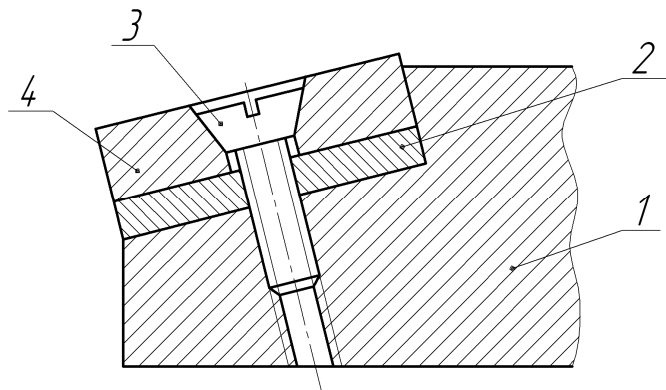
Закріплення пластини гвинтом: 1 – корпус; 2 – опорна пластина;
